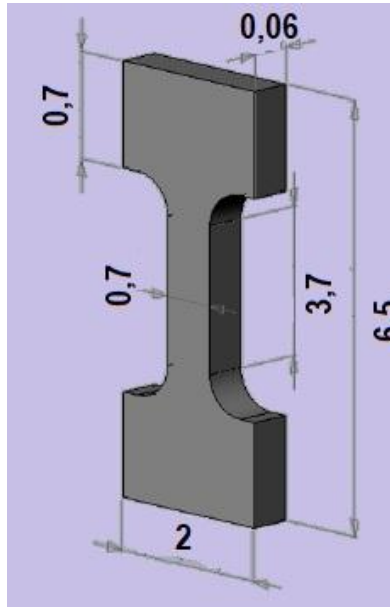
Diseño de probeta para ensayo de tracción (acotaciones en cm)
